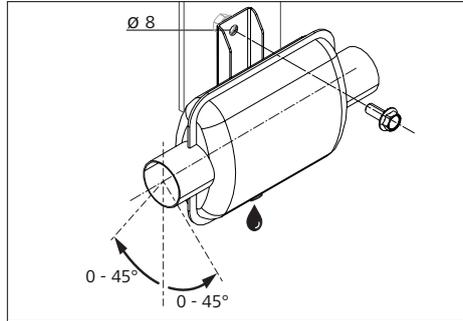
Einbaulage Abgasschalldämpfer (in mm)
